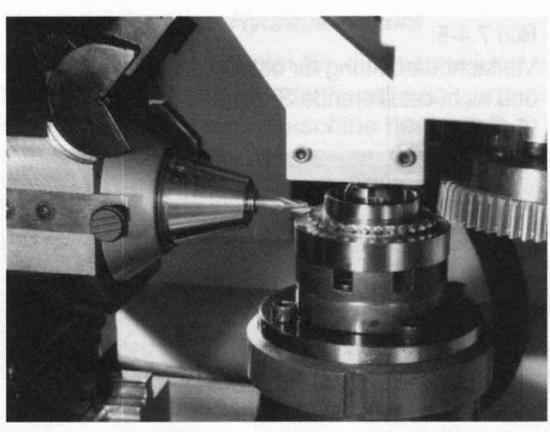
Kombinace odvalovacího frézování a obrážení na jednom stroji
